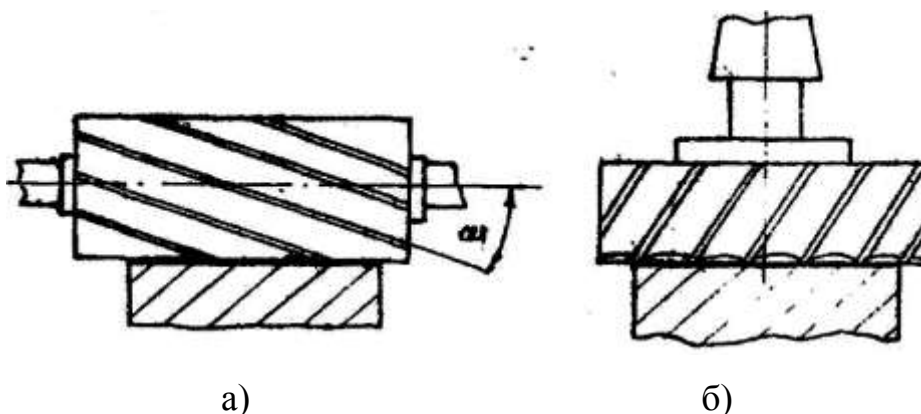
Фрезерование плоскостей цилиндрической (а) и торцевой (б) фрезами
